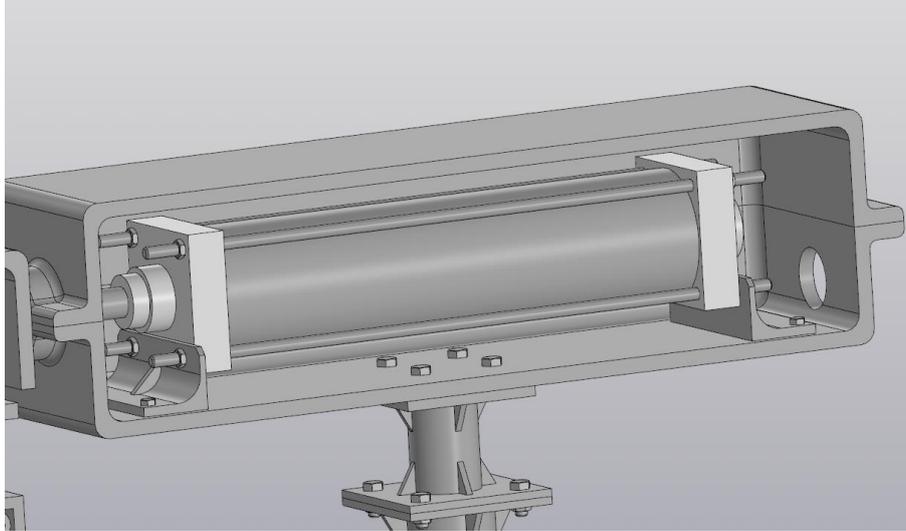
Пневмоцилиндр горизонтального перемещения внутри корпуса
